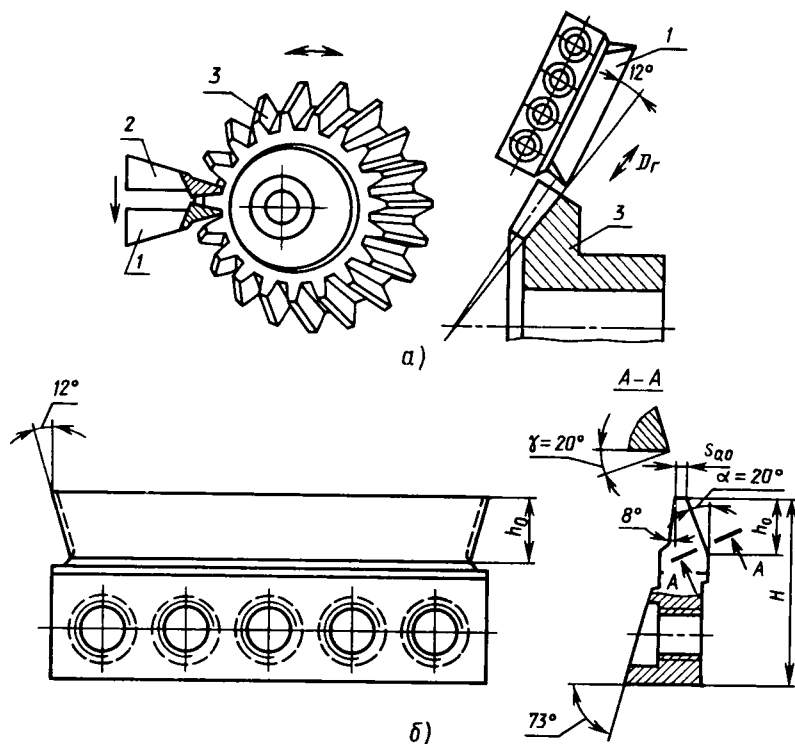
Резцы для нарезания зубьев прямозубого конического колеса
